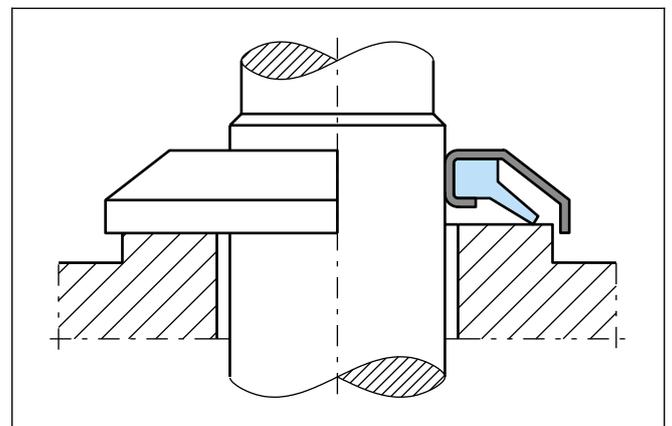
Ausführung der Lauffläche für senkrechte Wellen
